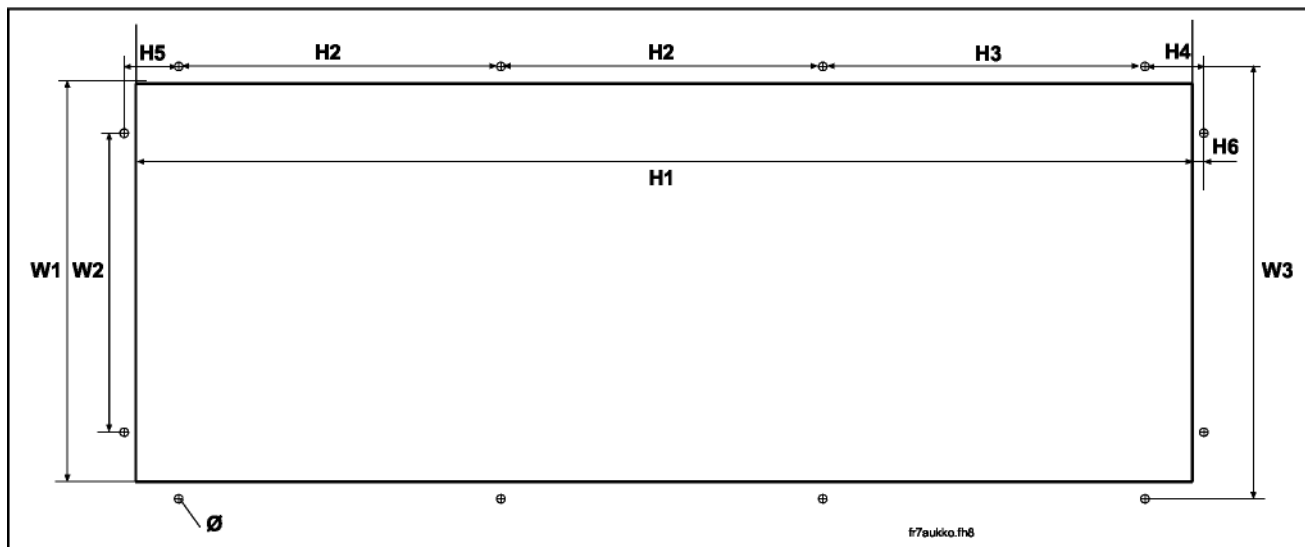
Abertura necessária para a montagem por flange, FR7
